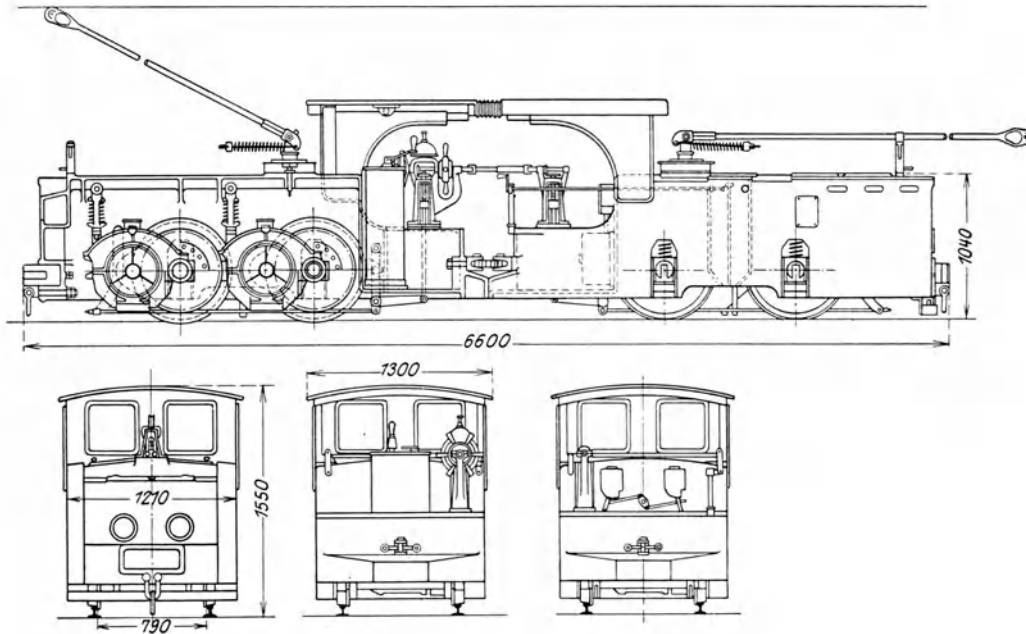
Doppel-Lokomotive für Stollenbetrieb. Motore hintereinander, Steuerung und Bremsung von einem Führersitz (Ganz).
